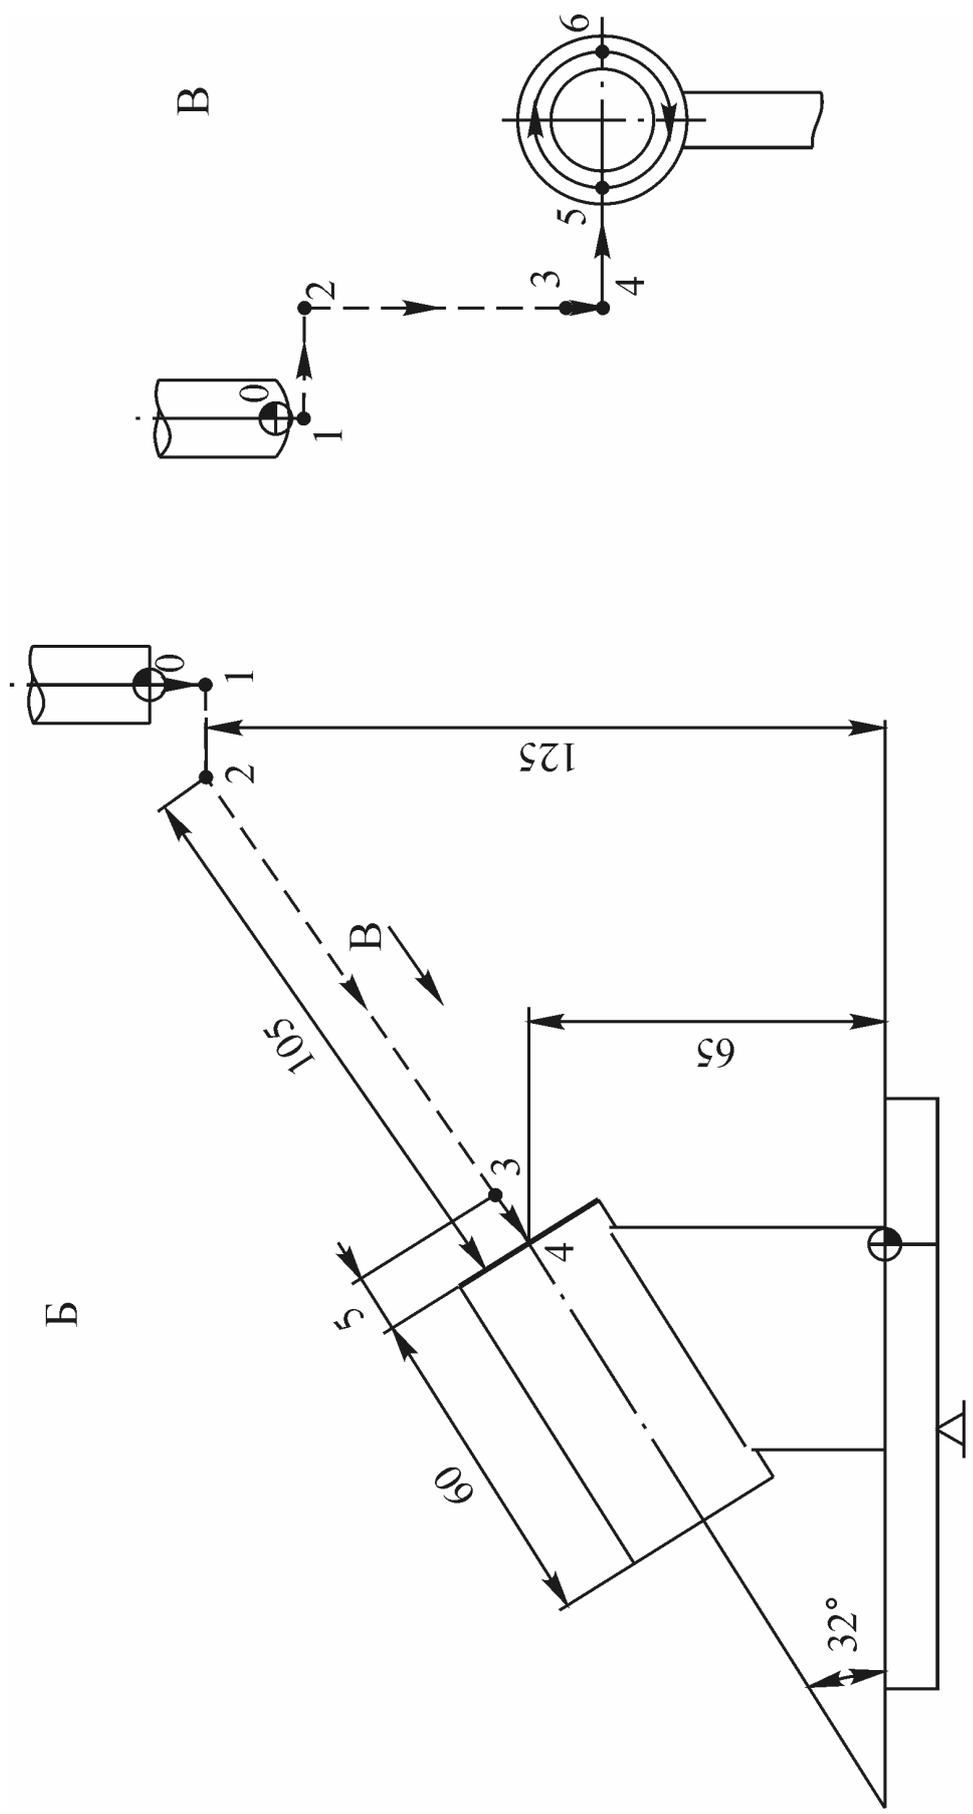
Расчетно-технологическая карта фрезерной обработки на станке с ЧПУ
